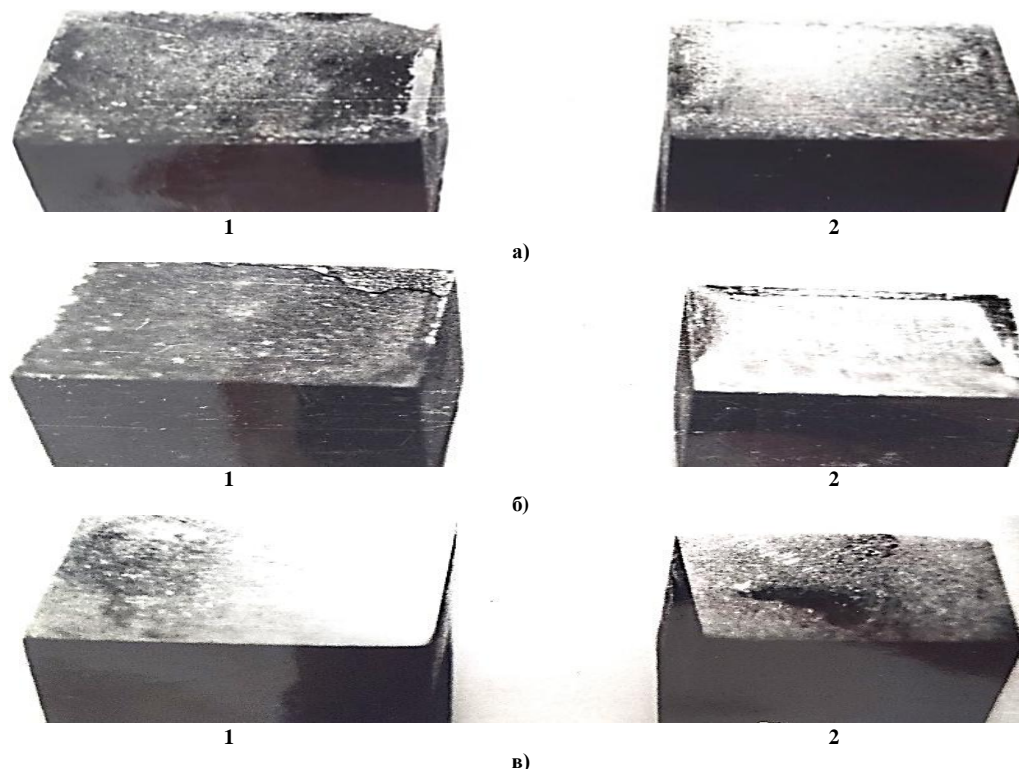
Фотография образцов, изготовленных из обрабатываемого материала сталь 40X.
